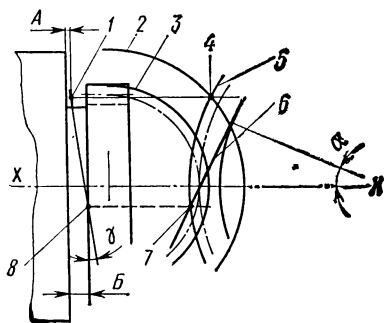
Определение угла скрепления при шевинговании зубчатых колес с закрытыми венцами
